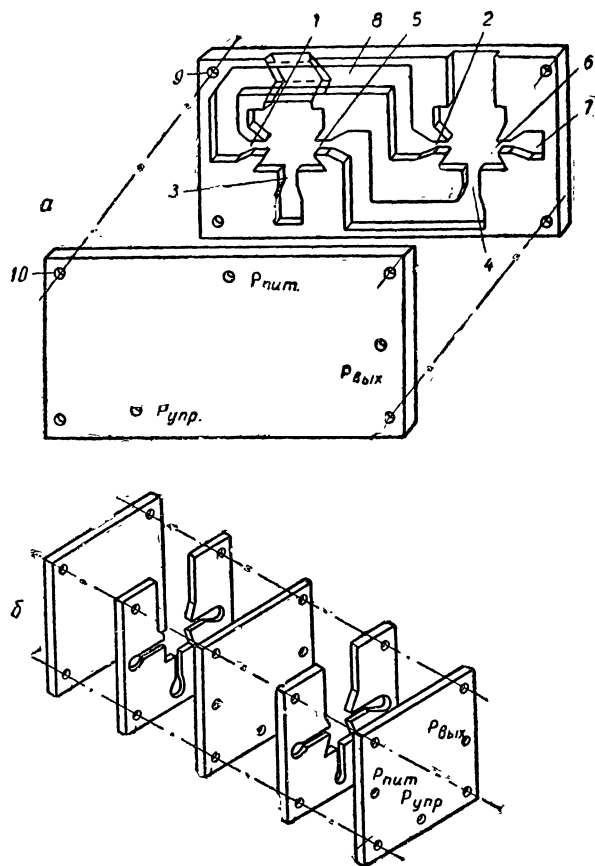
Схемы, поясняющие методику изготовления приборов пневмогидроавтоматики способом печатных (сборных) схем: а — однослойная конструкция (с одной рабочей пластиной); б — многослойная конструкция; 1—8, 8 — каналы в пластине; 7 — камера; 9 — рабочая пластина; 10 — крышка.
